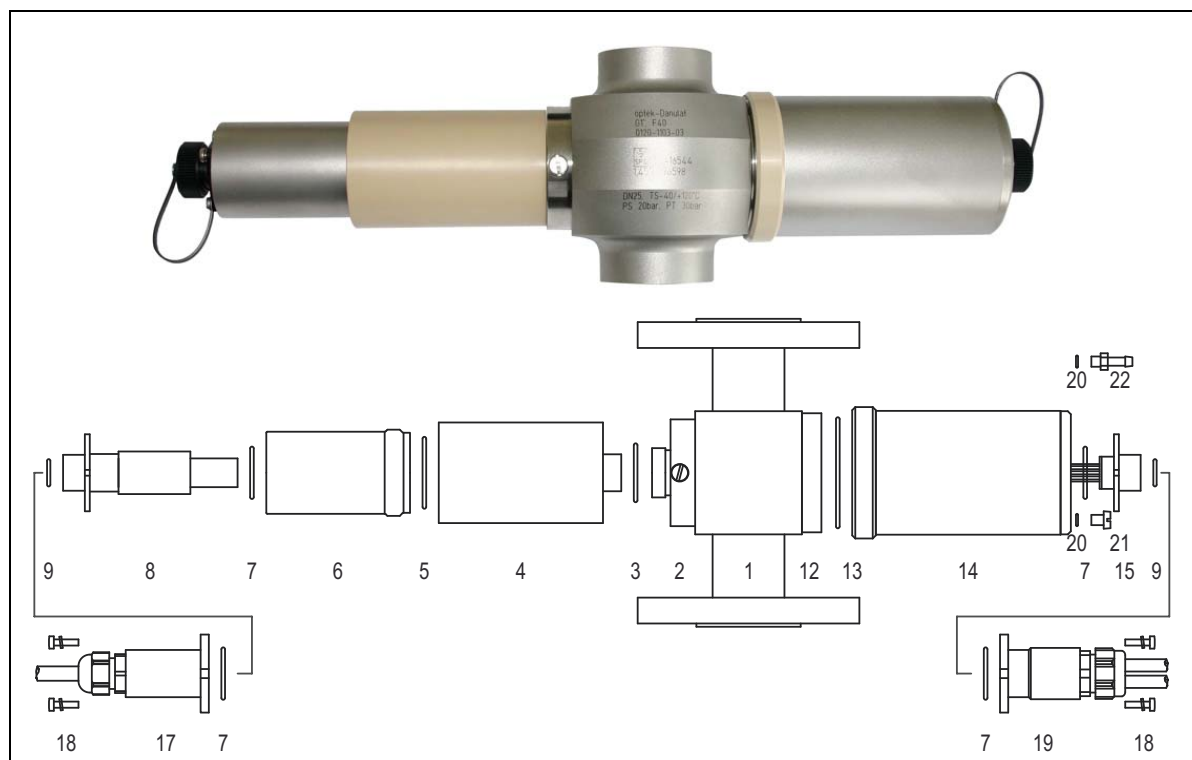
Foto y dibujo de despiece TF16-HT / TF16-HT-N
